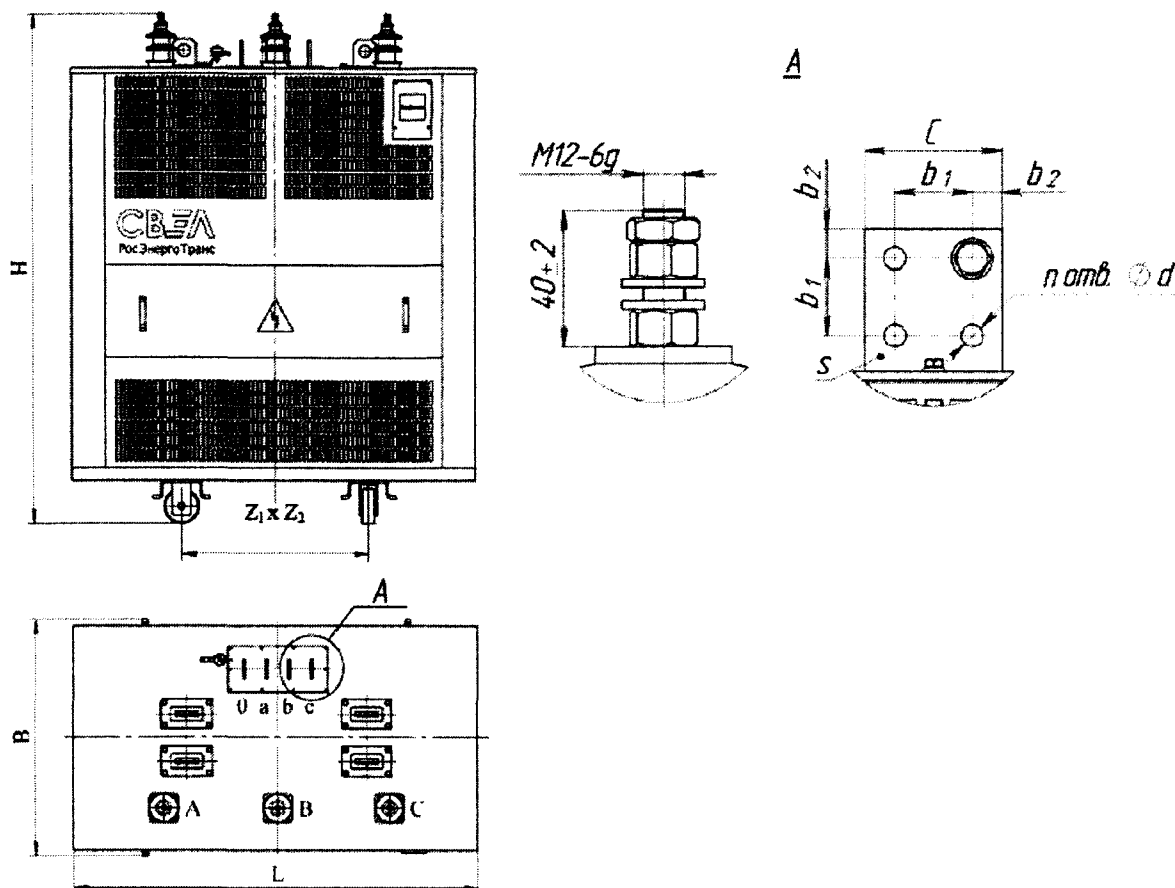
Общий вид и габаритно-установочные размеры трансформаторов серии ТСЗ с расположением вводов ВН и НН на крышке
